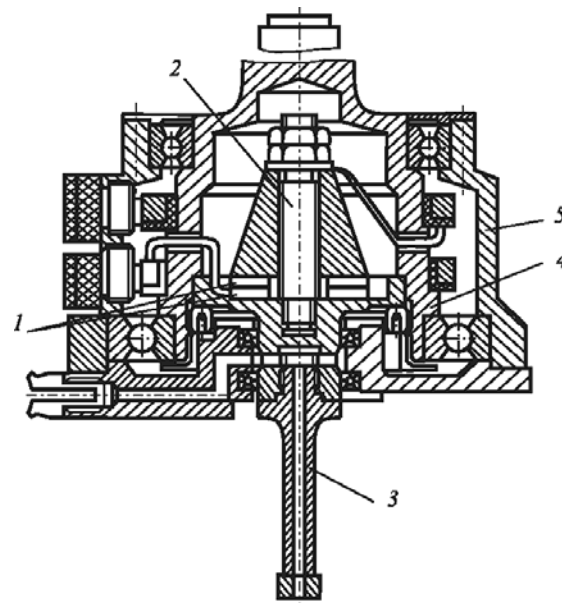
Устройство вращающейся акустической головки с пьезокерамическим преобразователем
